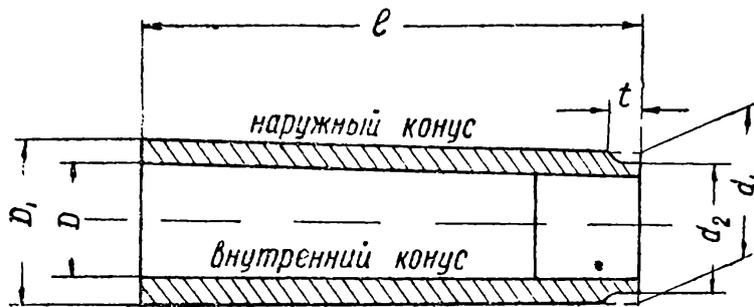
Переходная втулка для центров инструментов с конусной хвостовой частью.
